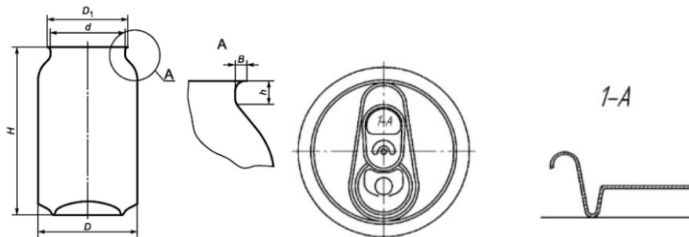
Конструкция алюминиевой банки и легковскрываемой крышкой
